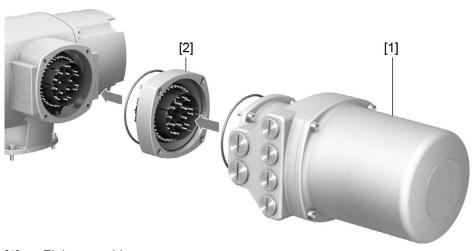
Halterahmen, Beispiel mit AUMA Rundsteckverbinder und Deckel
